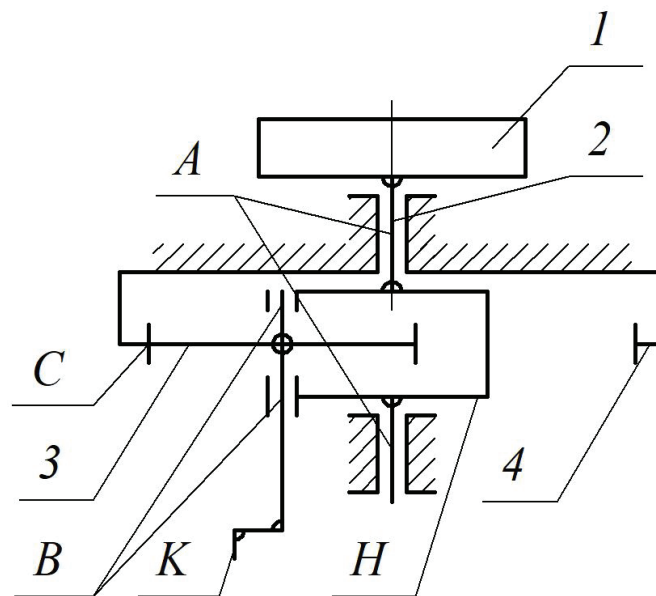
Кинематическая схема привода Шумахера Pro-Drive 85MНv GK ASM04:
